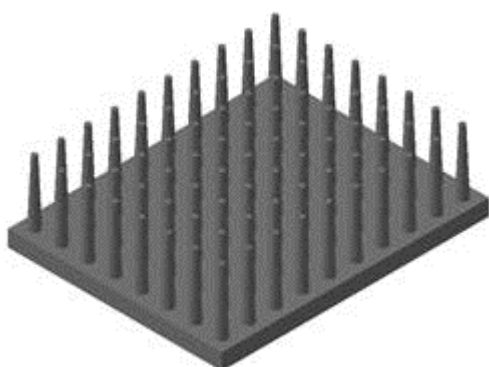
Поверхность, развитая штырьками (коридорное расположение)
